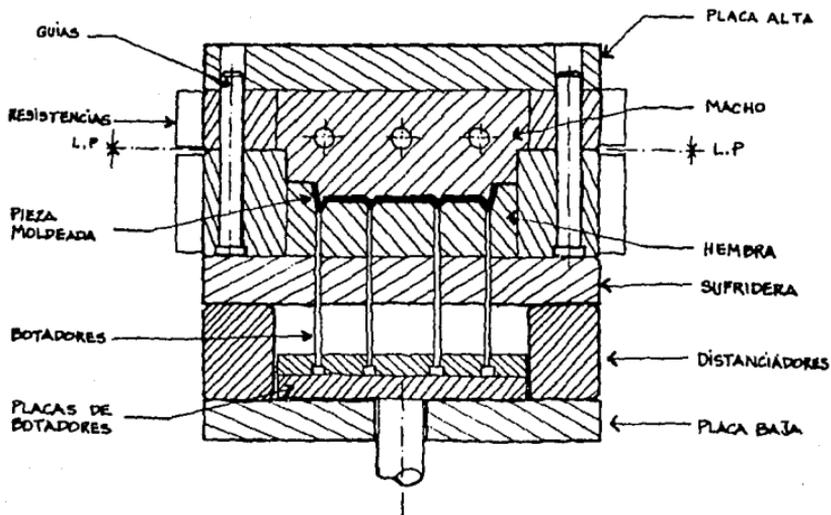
Corte de un molde de Compresión donde se señalan sus partes más significativas
